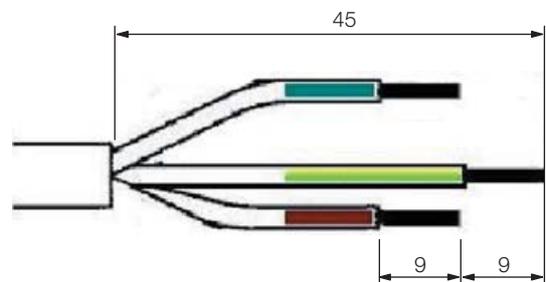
Maße zum Entfernen der Gummiummantelung und der Isolierung
